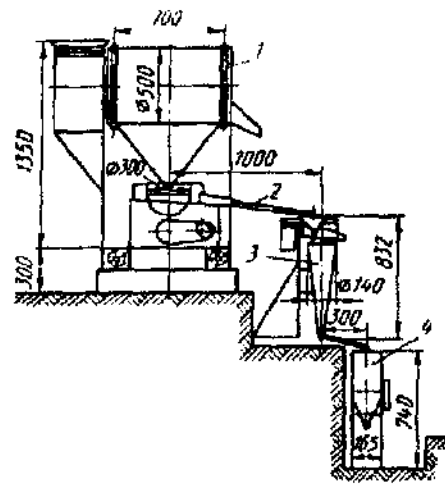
Схема опытной обогащательной установки для обработки проб:
